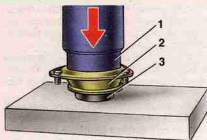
Обжим корпуса опоры: 1 – оправка; 2 – верхняя опора; 3 – упор
